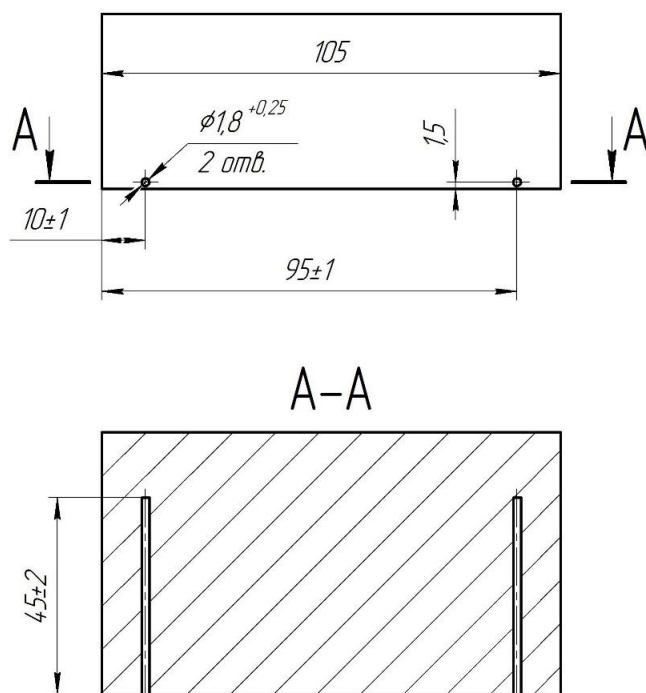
Чертеж части канала с отверстиями в стенке для крепления термопар
